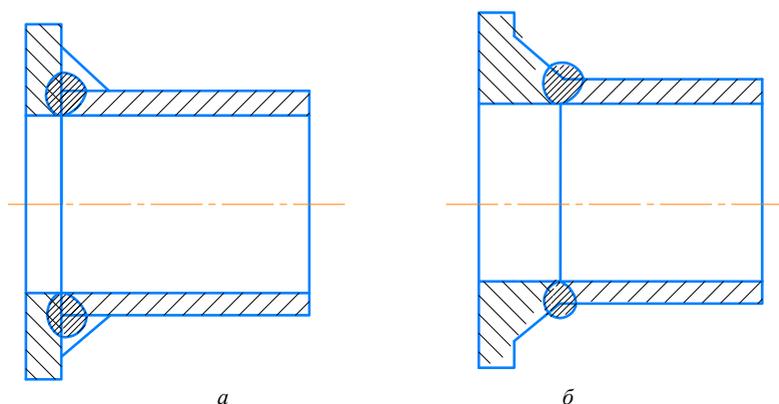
Сварное соединение фланца с трубой: *а* – фланец плоский; *б* – фланец с отбортовкой
